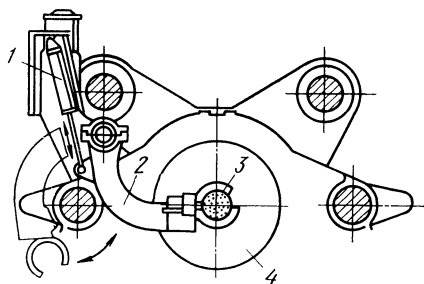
Механизированные устройства для нанесения плавящихся порошкообразных смазок на боковую поверхность нагретых заготовок [164]
